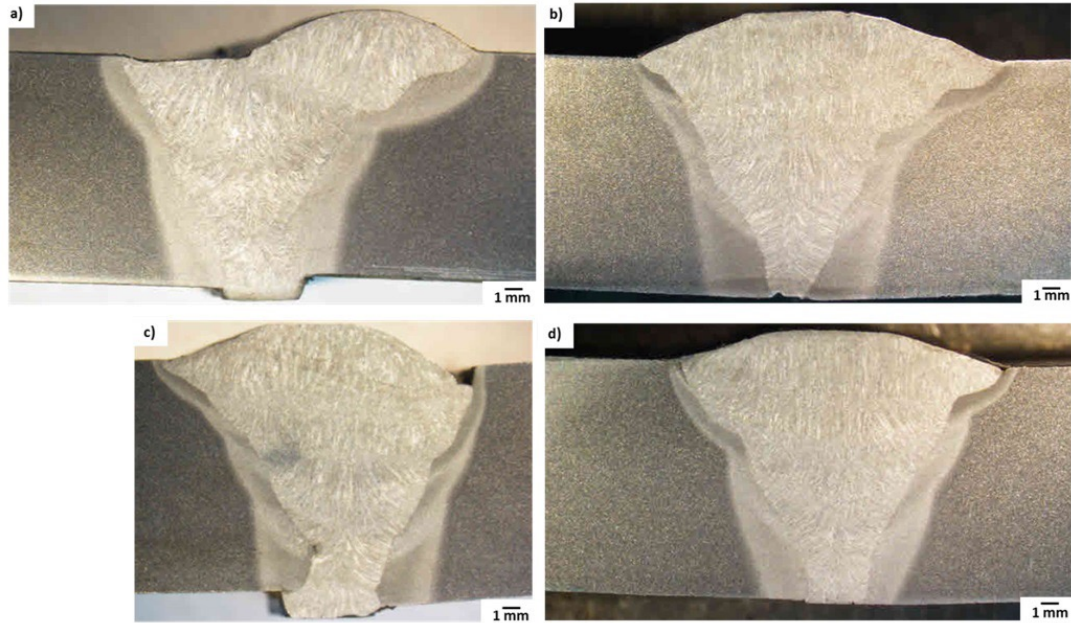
Macrografías de uniones soldadas a tope en condición de soldadura A (201 A, 27 V, Velocidad de soldadura 38.5 cm /min) con soldadura robótica GMAW con diferentes movimientos de soldadura: a) lineal, b) sinusoidal, c) circular y d) triangular [12].
